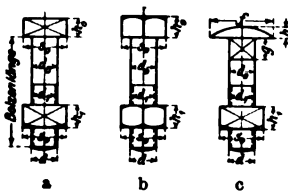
a/b Maschinenschrauben, c Schloßschraube.
